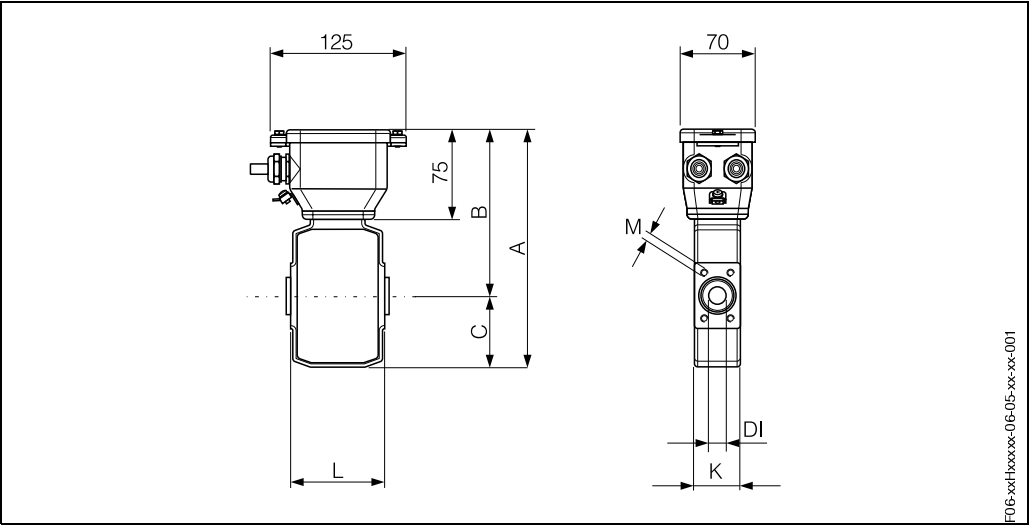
Dimensiones del Promag H / DN 2...25 (versión separada)
